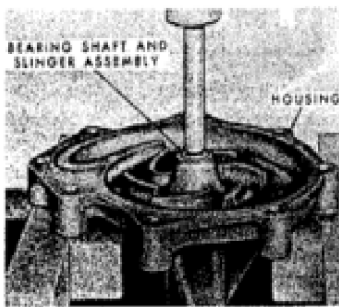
View tonen schacht en lager as- ssembly wordt geperst uit waaier en behuizing.
